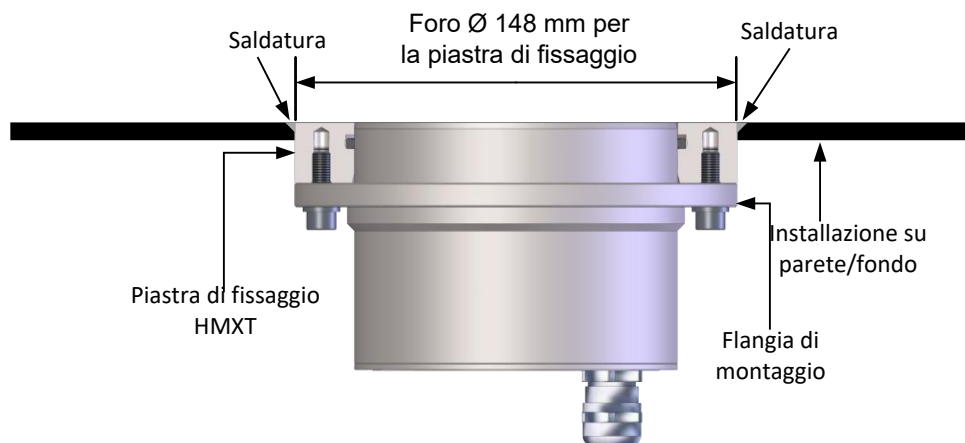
Installazione del sensore (piastra di fissaggio montata a filo)
